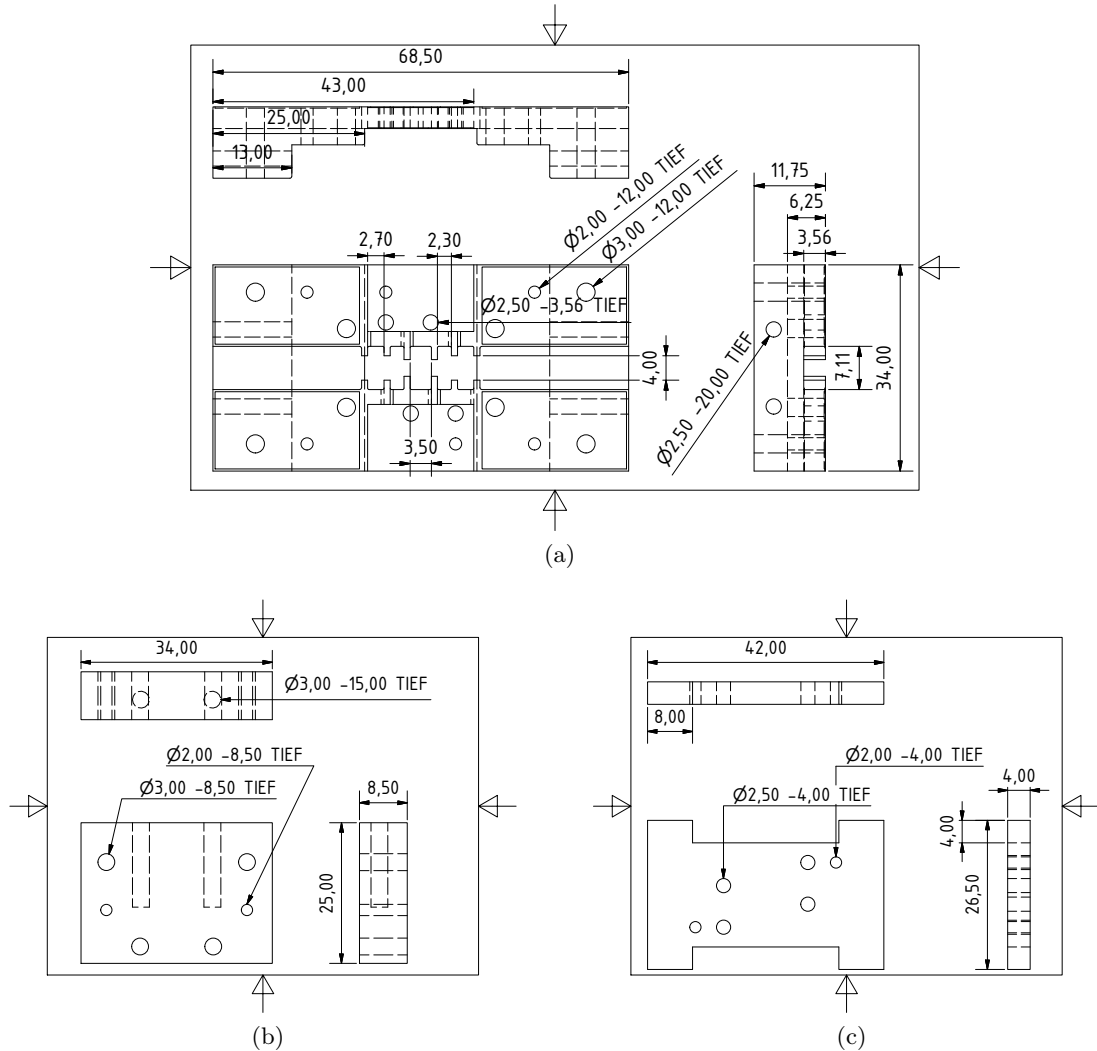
Zeichnungen der Messingteile des Hohlleiterfilters, mit den wichtigsten Dimensionen in mm.
